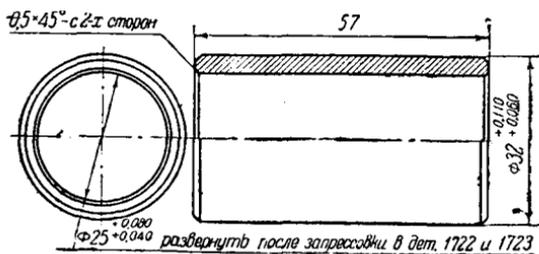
Дет. 1724. Втулка двуплечего рычага
